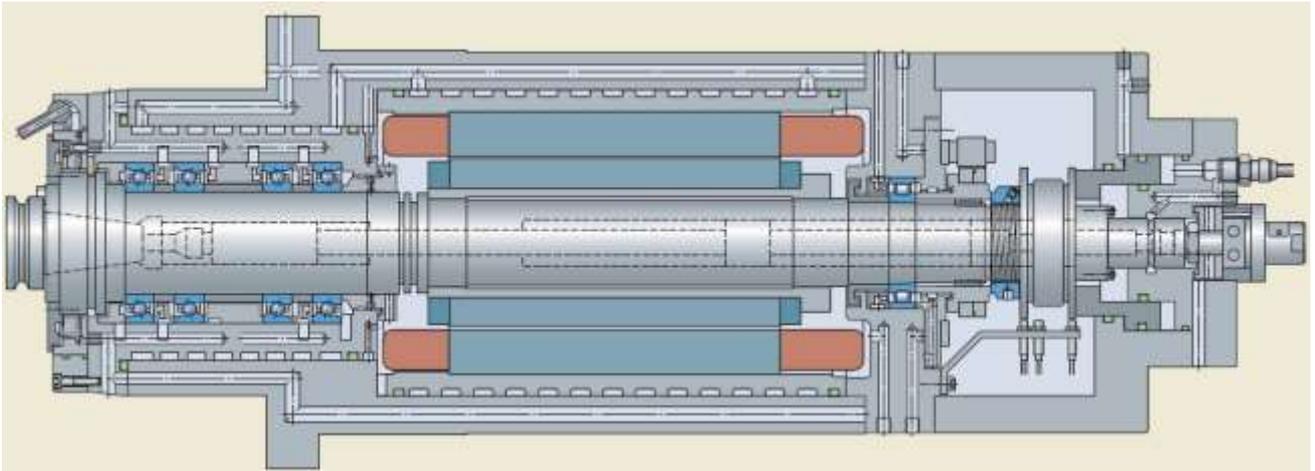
Схема мотор-шпинделя горизонтального обрабатывающего центра
